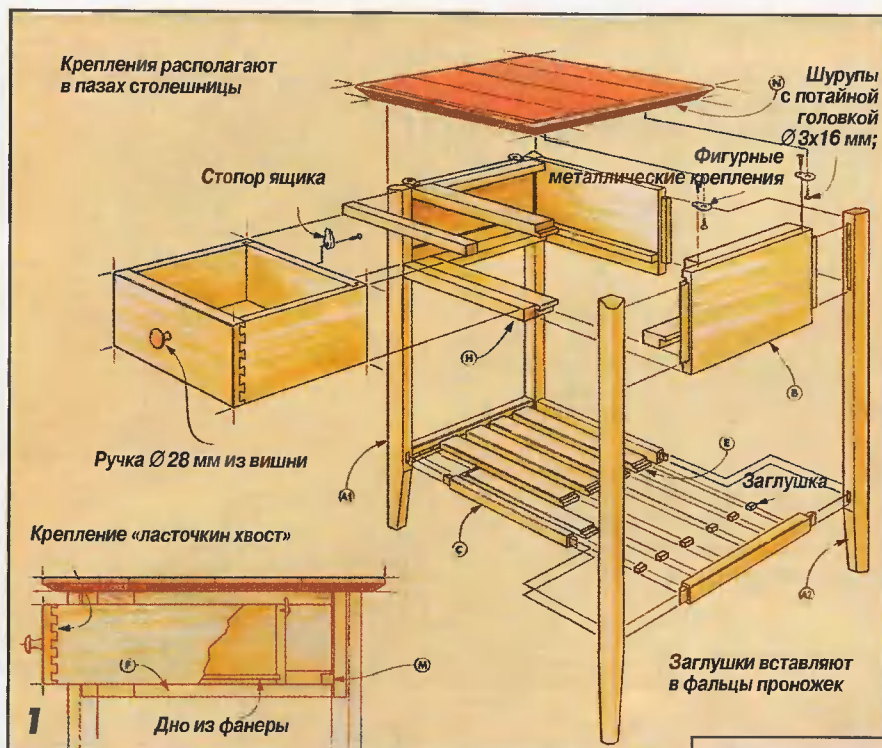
Столик высотой 610 мм со столешницей 480x480 мм. А1 — ножка передняя; А2 — ножка задняя; В — царги; С — проножки; D — поперечины проема ящика; E — перекладки полки; F — направляющие; G — ограничители; H — лицевые бруски; I — фасад ящика; J — задняя стенка ящика; K — боковины ящика; L — днище ящика (фанера); M — упор ящика; N — столешница.
